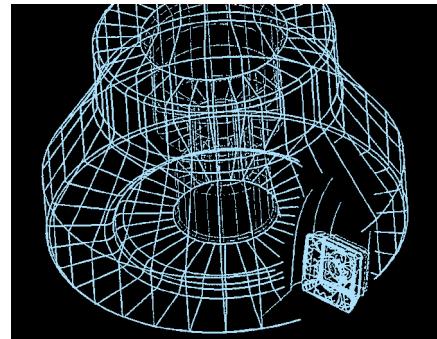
Implantation d'une plaquette sur une fraise à surfacer
